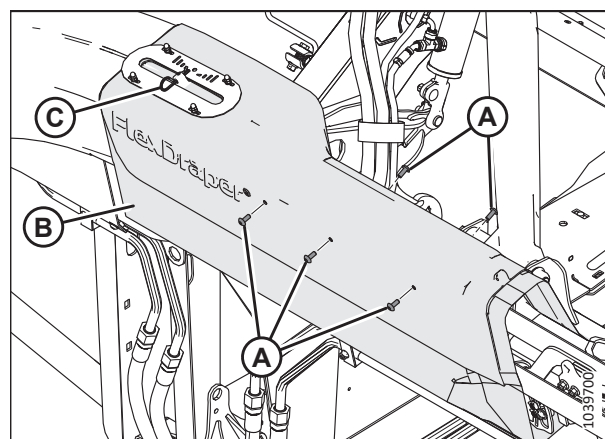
Levý kryt spojovacího ústrojí – zadní část adaptéru
